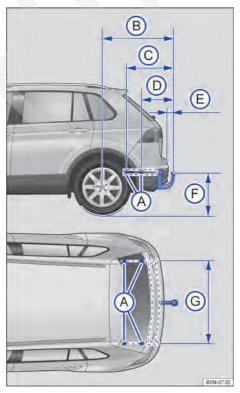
Dimensões e pontos de fixação para instalar um dispositivo de reboque posteriormente.
